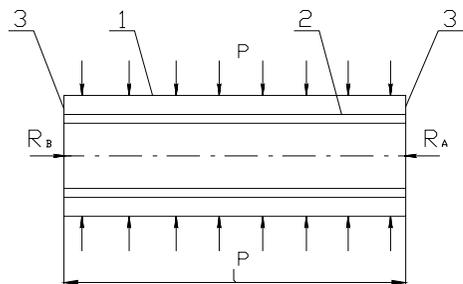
Схема нагружения элементов топки водотрубно-дымогарного котла:
